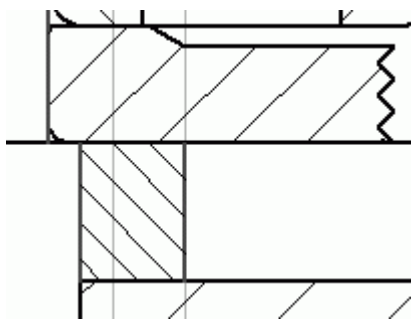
Распорное кольцо для осевой фиксации зубчатого колеса
